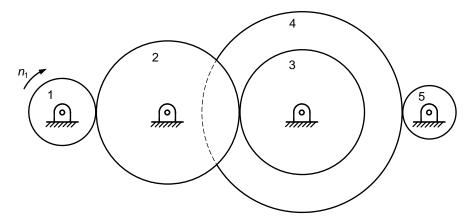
Trem de engrenagens cilíndricas normal composto.
